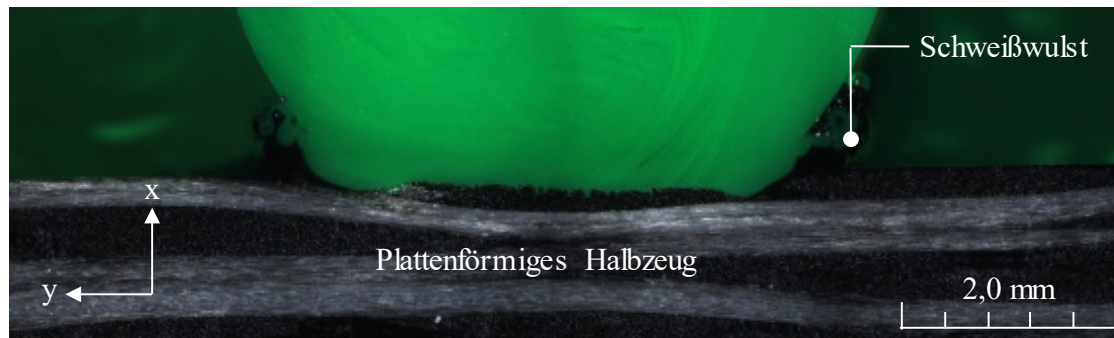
Schliffbild der Schweißverbindung PP-GF/PP
